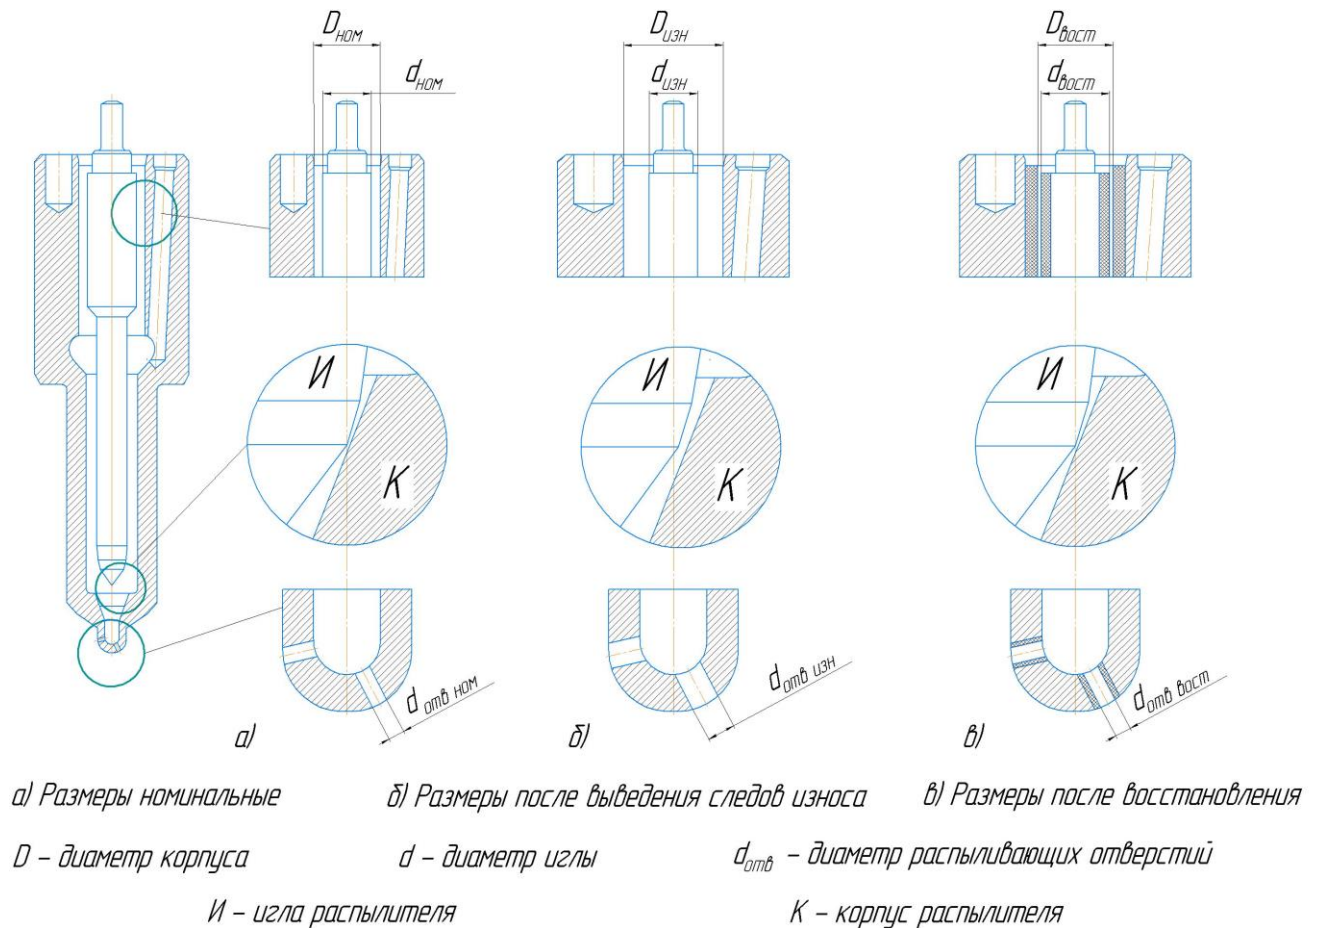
Схема геометрических размеров деталей распылителя форсунки:
